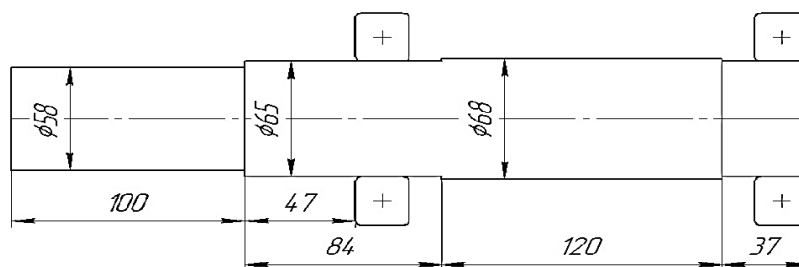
Размеры и расположение подшипников на валу редуктора
